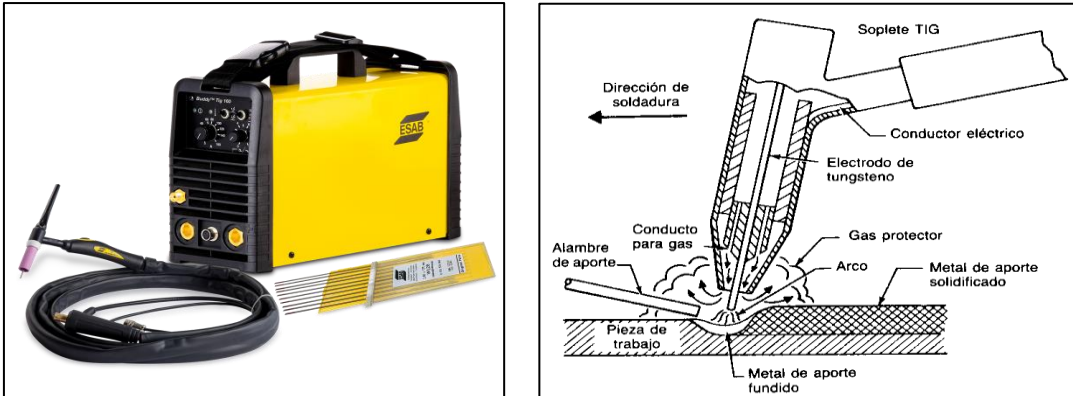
Equipo de soldadura TIG y soldadura TIG
